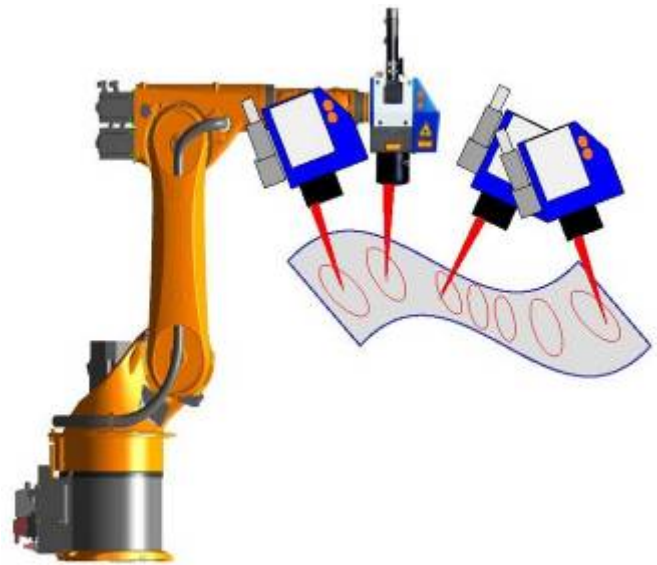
Scanner-Schweißen am Roboter [43]
